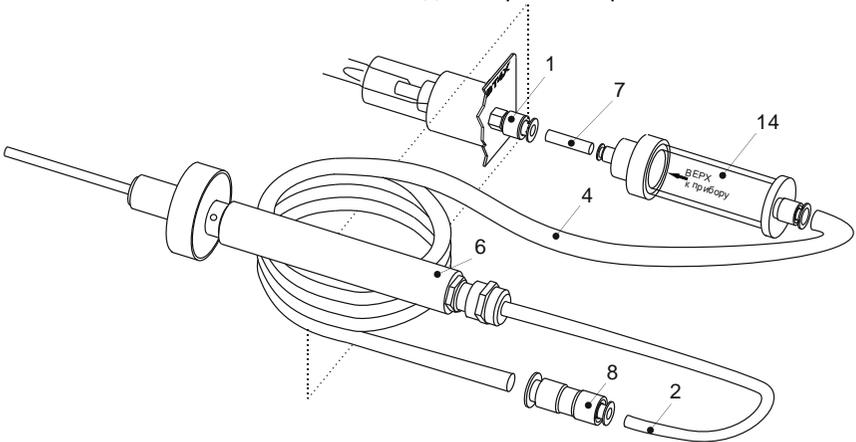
Схема соединения удлинителя и устройства защиты детектора с газоанализатором
